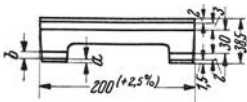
Werkaufriß zu Abb. 316. a = Bearbeitungszugabe für das Metallmodell; b = Bearbeitungszugabe für den Abguß.
